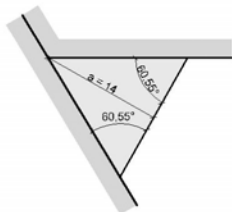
Untersuchte Schweißnahtgeometrien für a = 14mm
